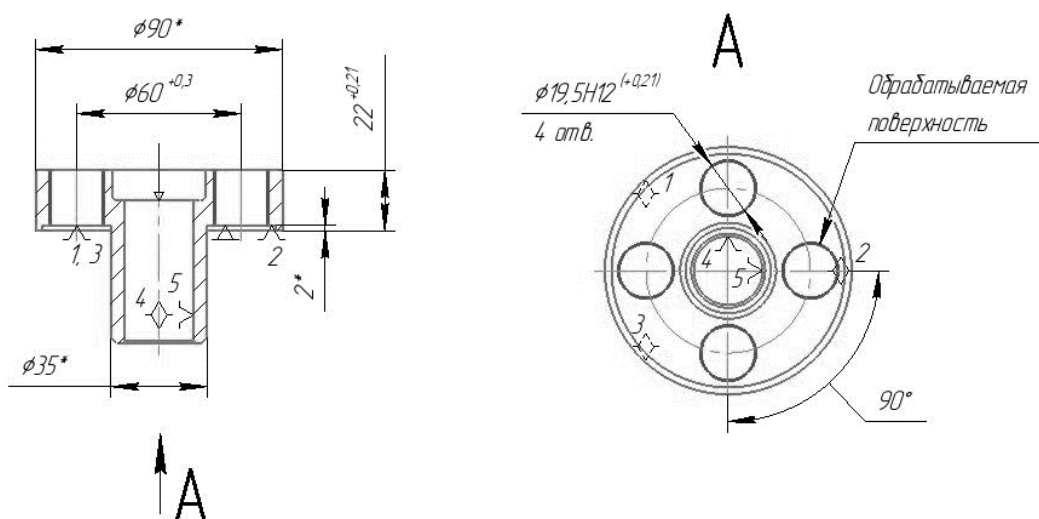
Операционный эскиз детали «Полумуфта»
